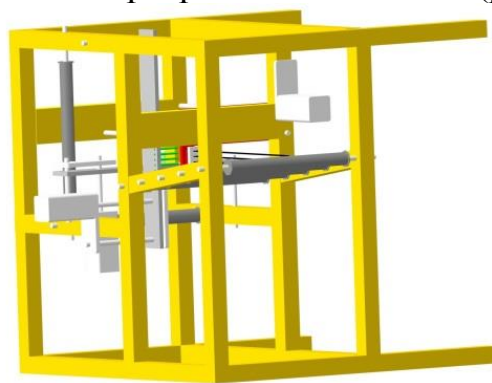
Макет станка для изготовления 3D-ткани.
